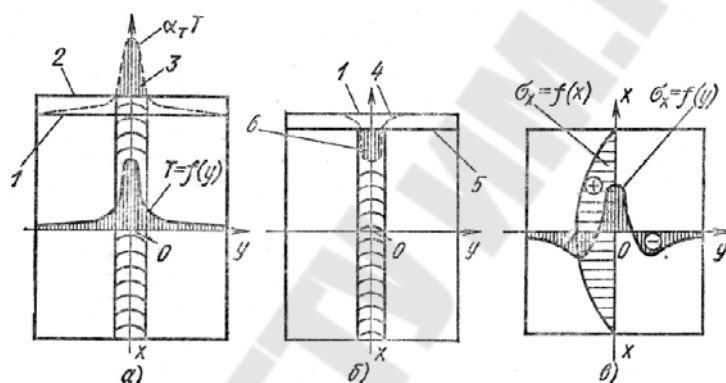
Схема напряженного состояния сварного шва
